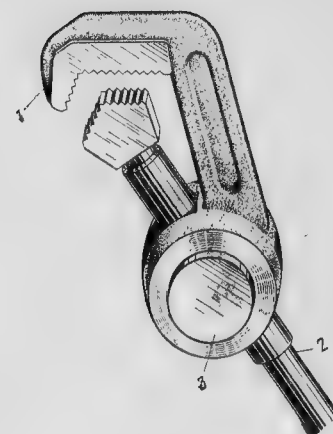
1 — скоба накидная; 2 — ручка; 3 — гайка
